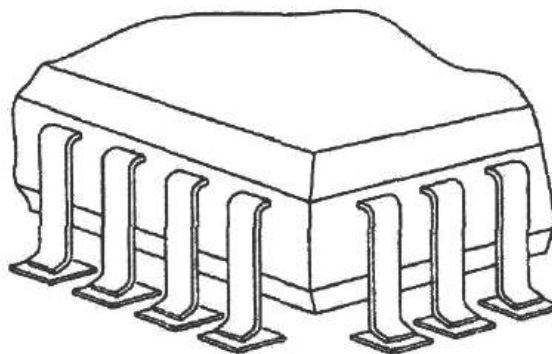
Корпус TQFP, що розташований на ПП
